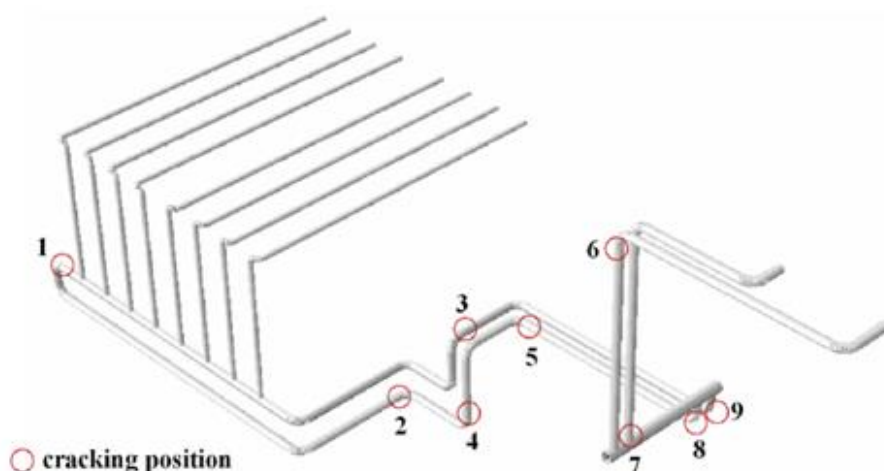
Localización de las grietas dentro de la instalación.
